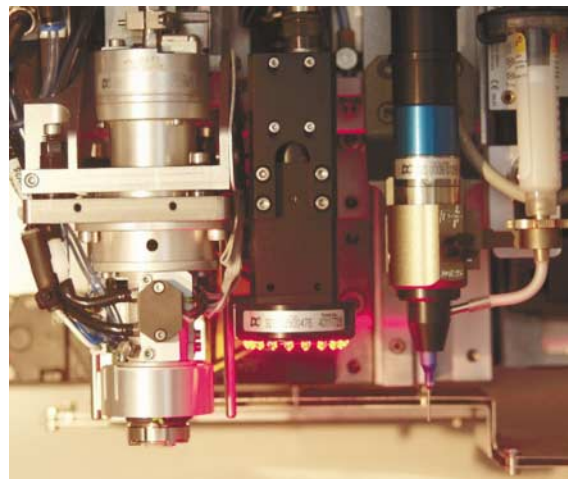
Hochgenaue Dispenser und geheizte, präzise positionierte Bondköpfe mit Werkzeugwechsler ermöglichen hohe Produktqualität und hohen Durchsatz
